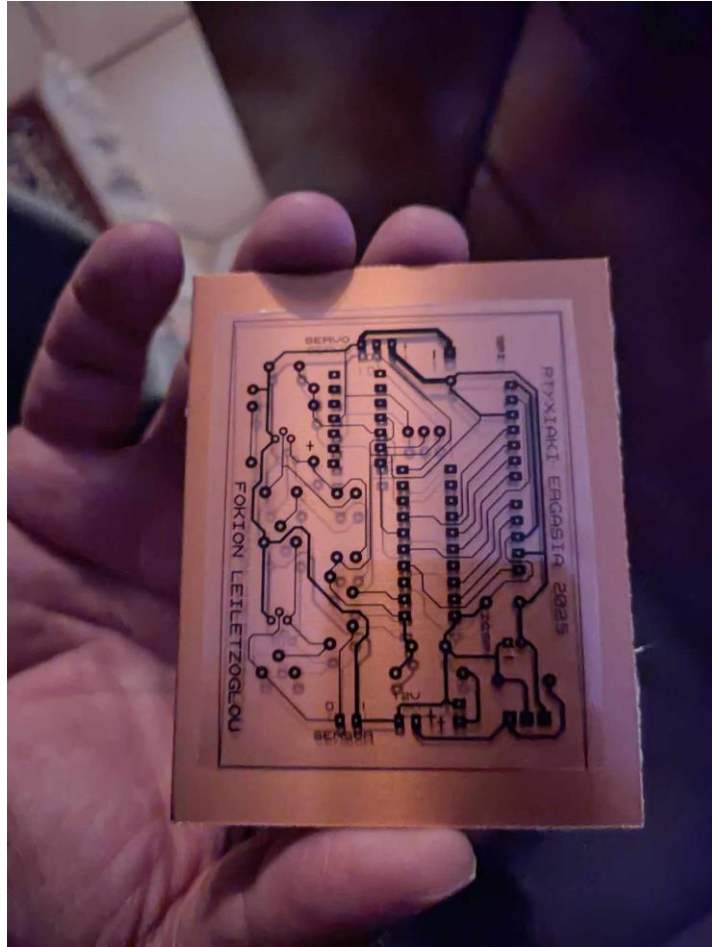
Σχεδιασμός PCB (Printed Circuit Board)
